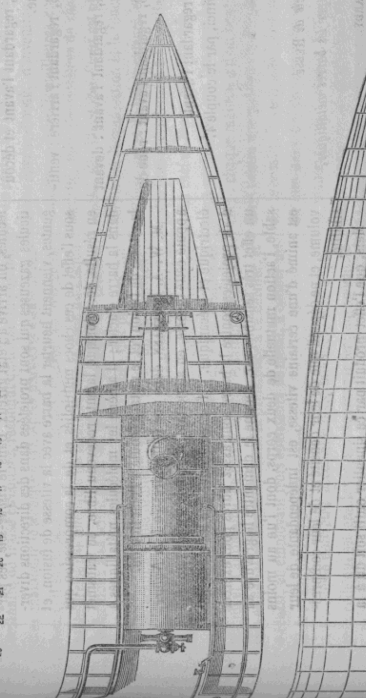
Vue horizontale de la cabine de la chaudière et des machines motrices.
